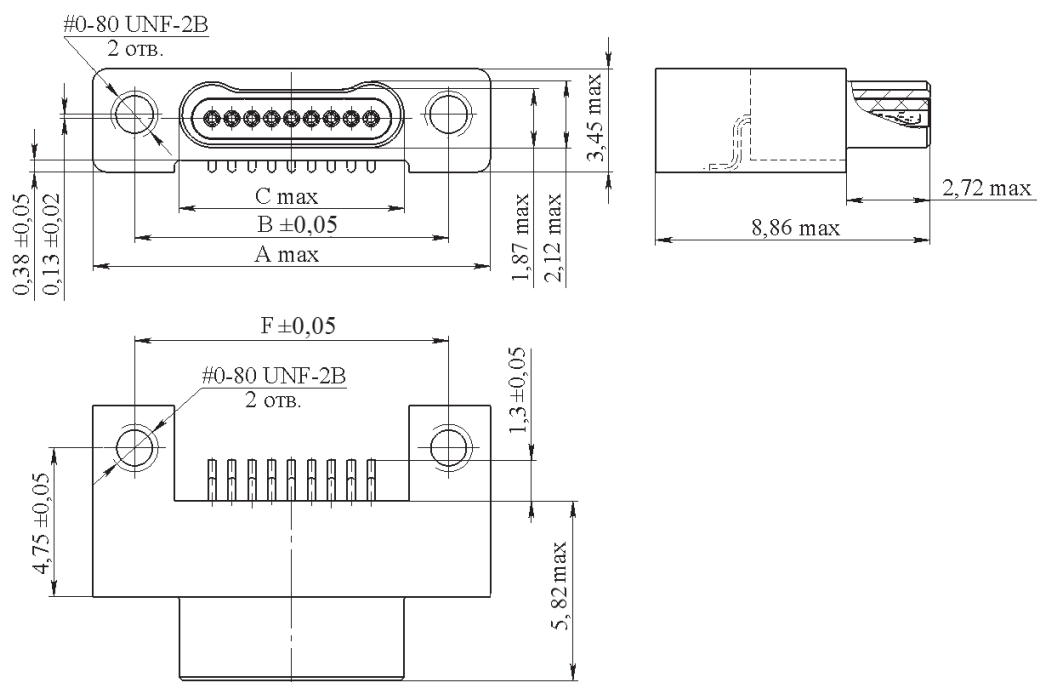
Соединитель СП450-02...1...Ш1...
